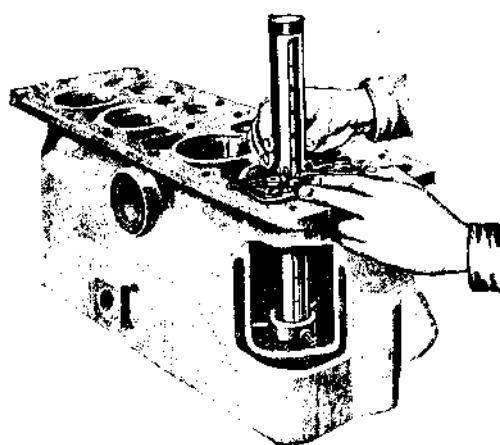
Прибор для измерения цилиндров фирмы Barriguand & Marce.
